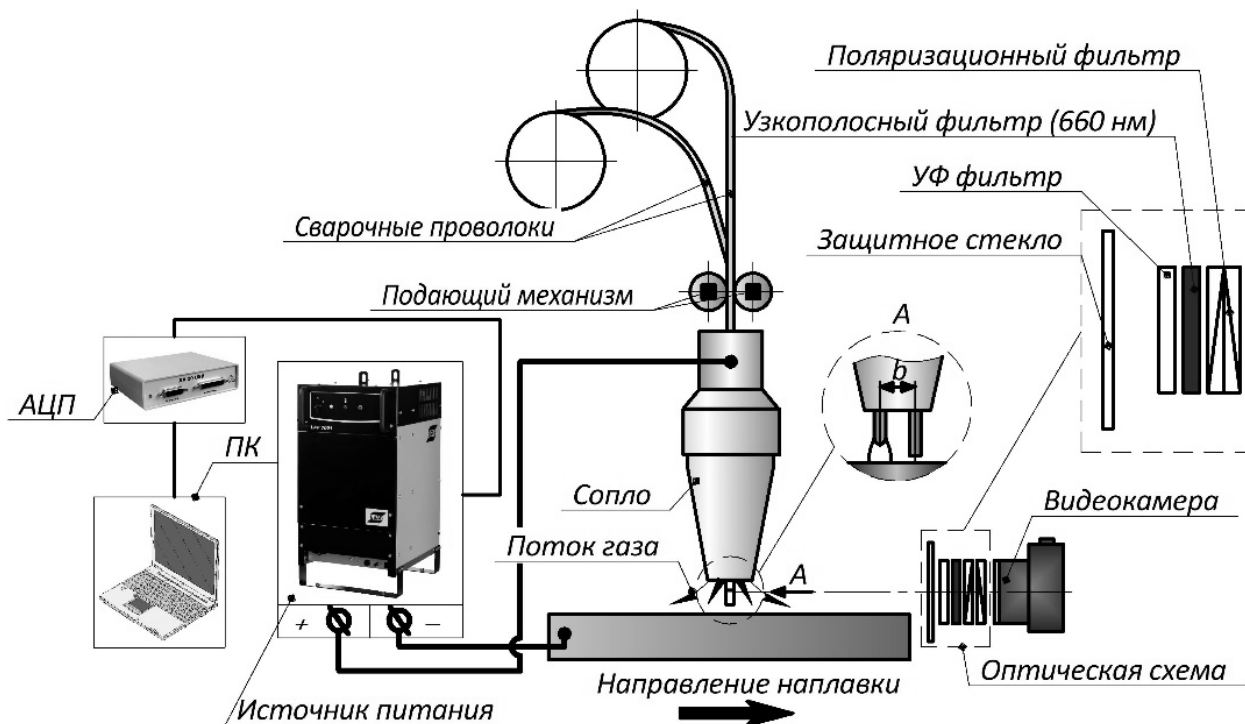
Схема исследования дугового промежутка и переноса электродного металла при наплавке с регистрацией сварочного тока и напряжения
